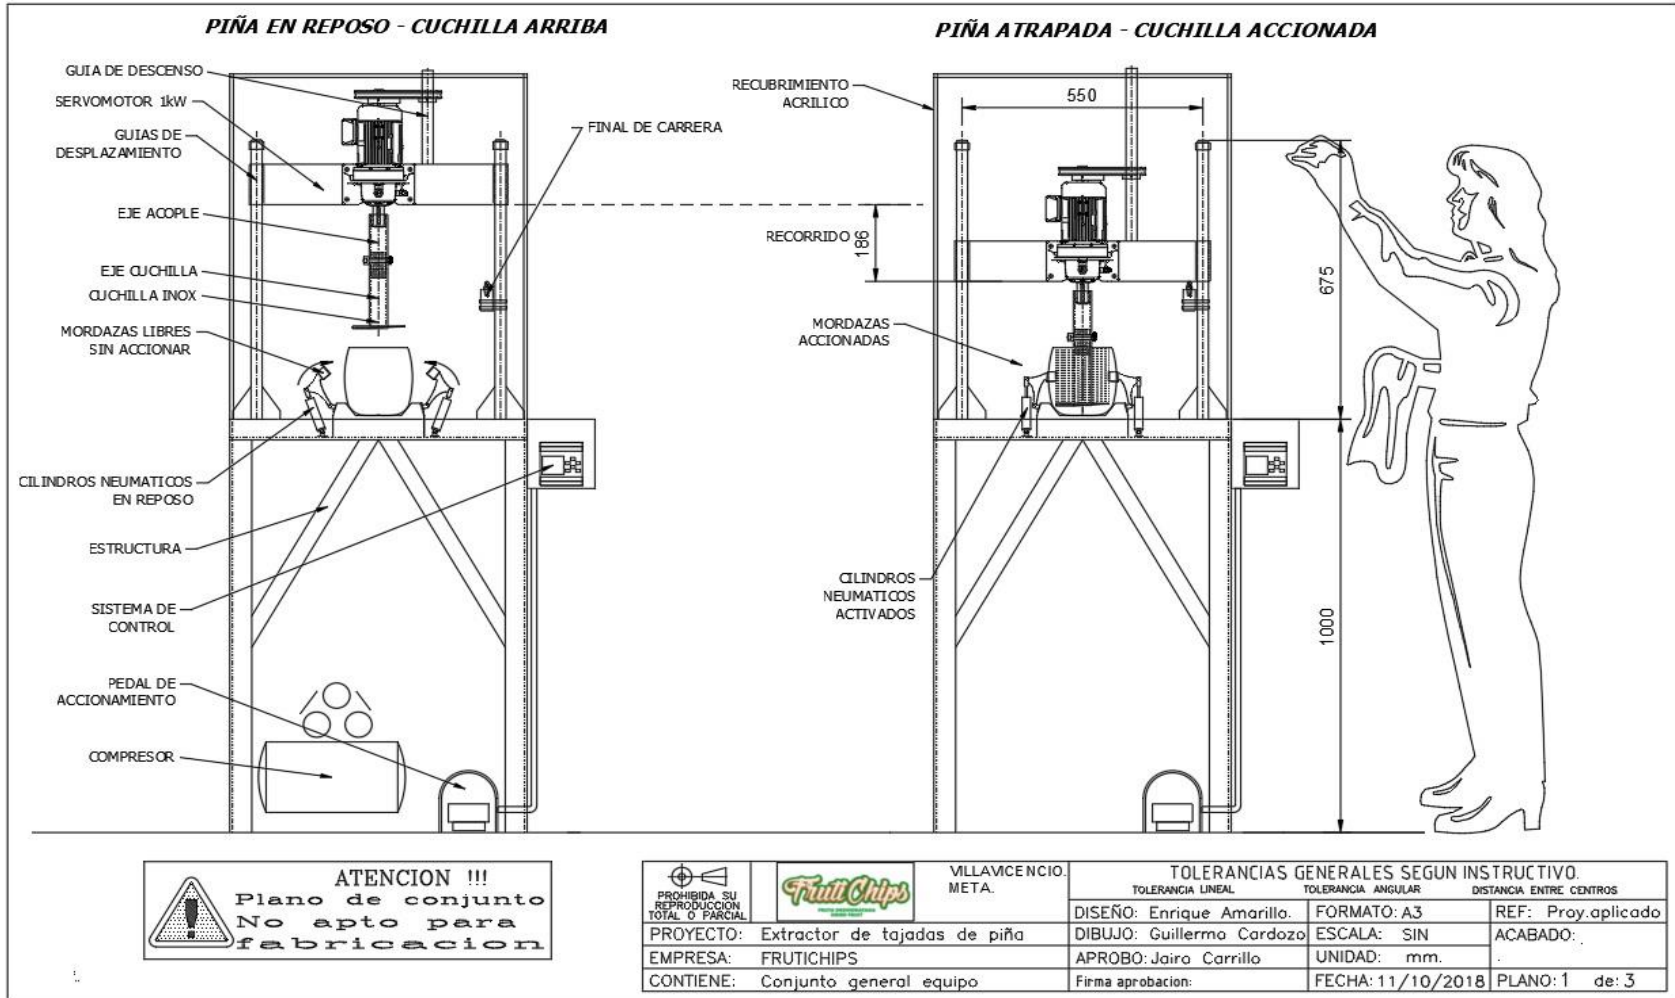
Plano de conjunto general equipo, estado en reposo y estado en funcionamiento.
